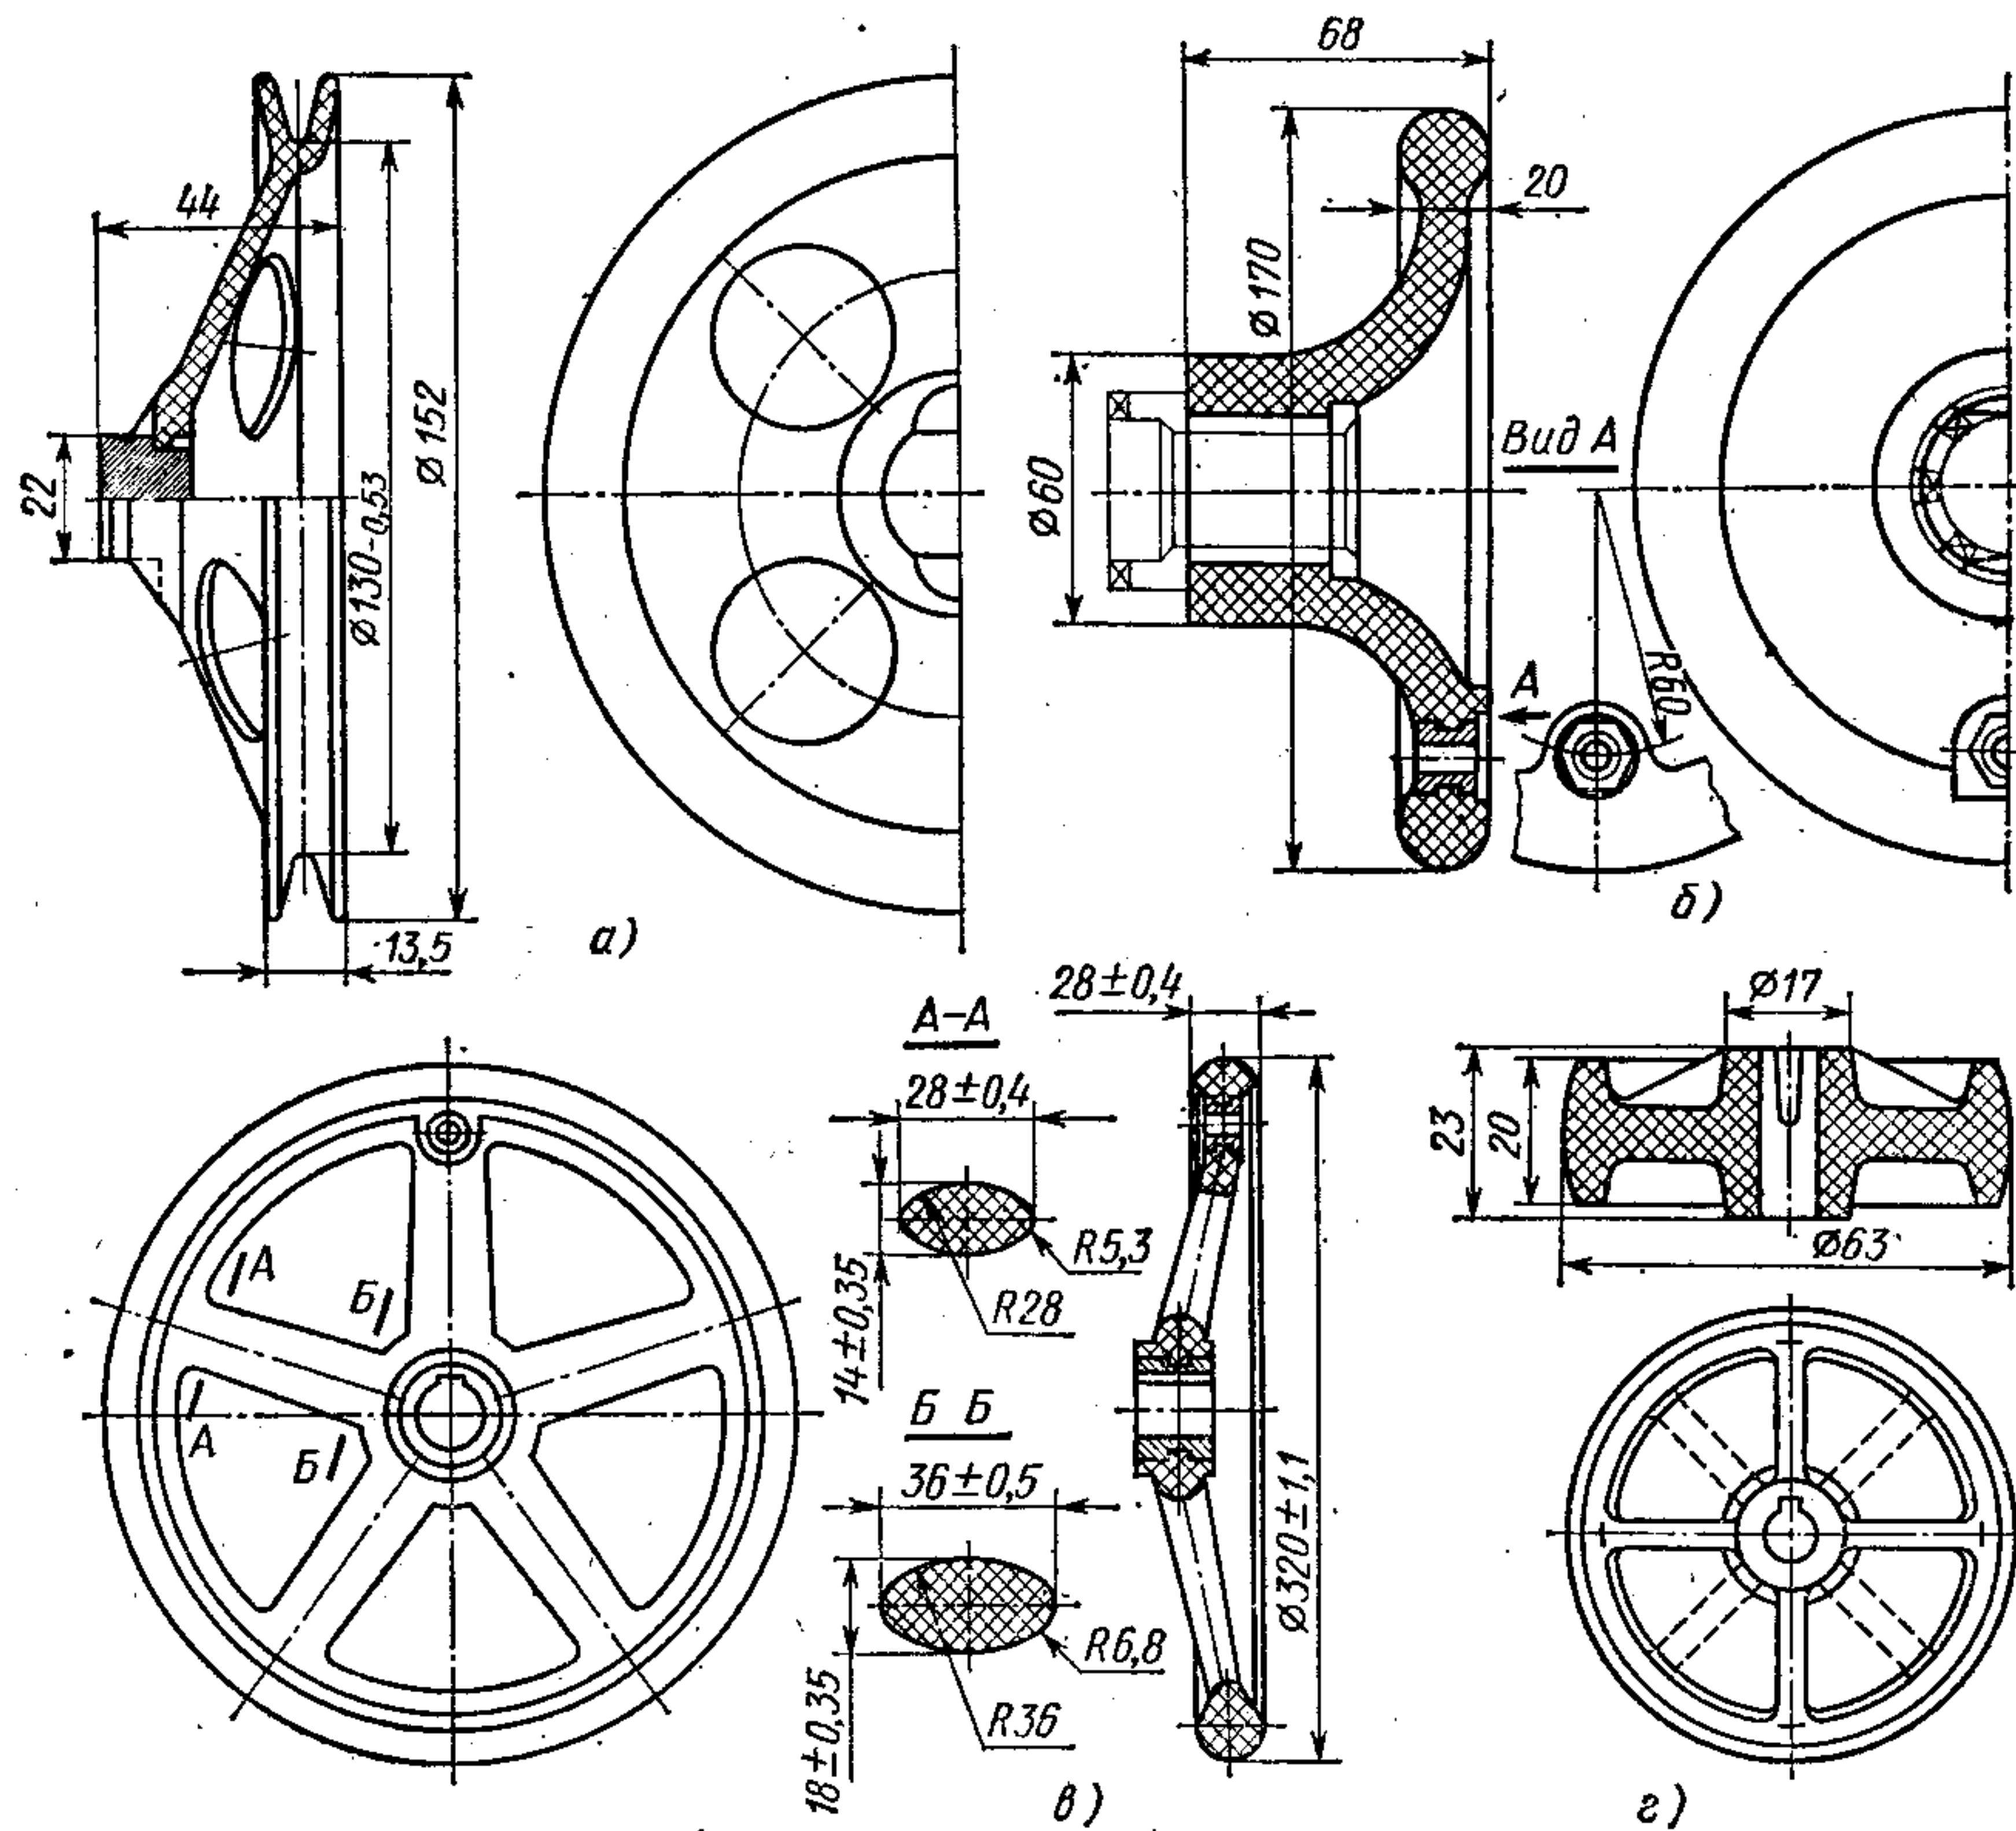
Примеры правильных конструкций: а — шкив пульсатора (пресс-материал 01-040-02); б — маховик без спиц (волокнит); в — маховик со спицами (пресс-материал 03-010-02); г — ролик ходовой (пресс-материал 01-040-02)
